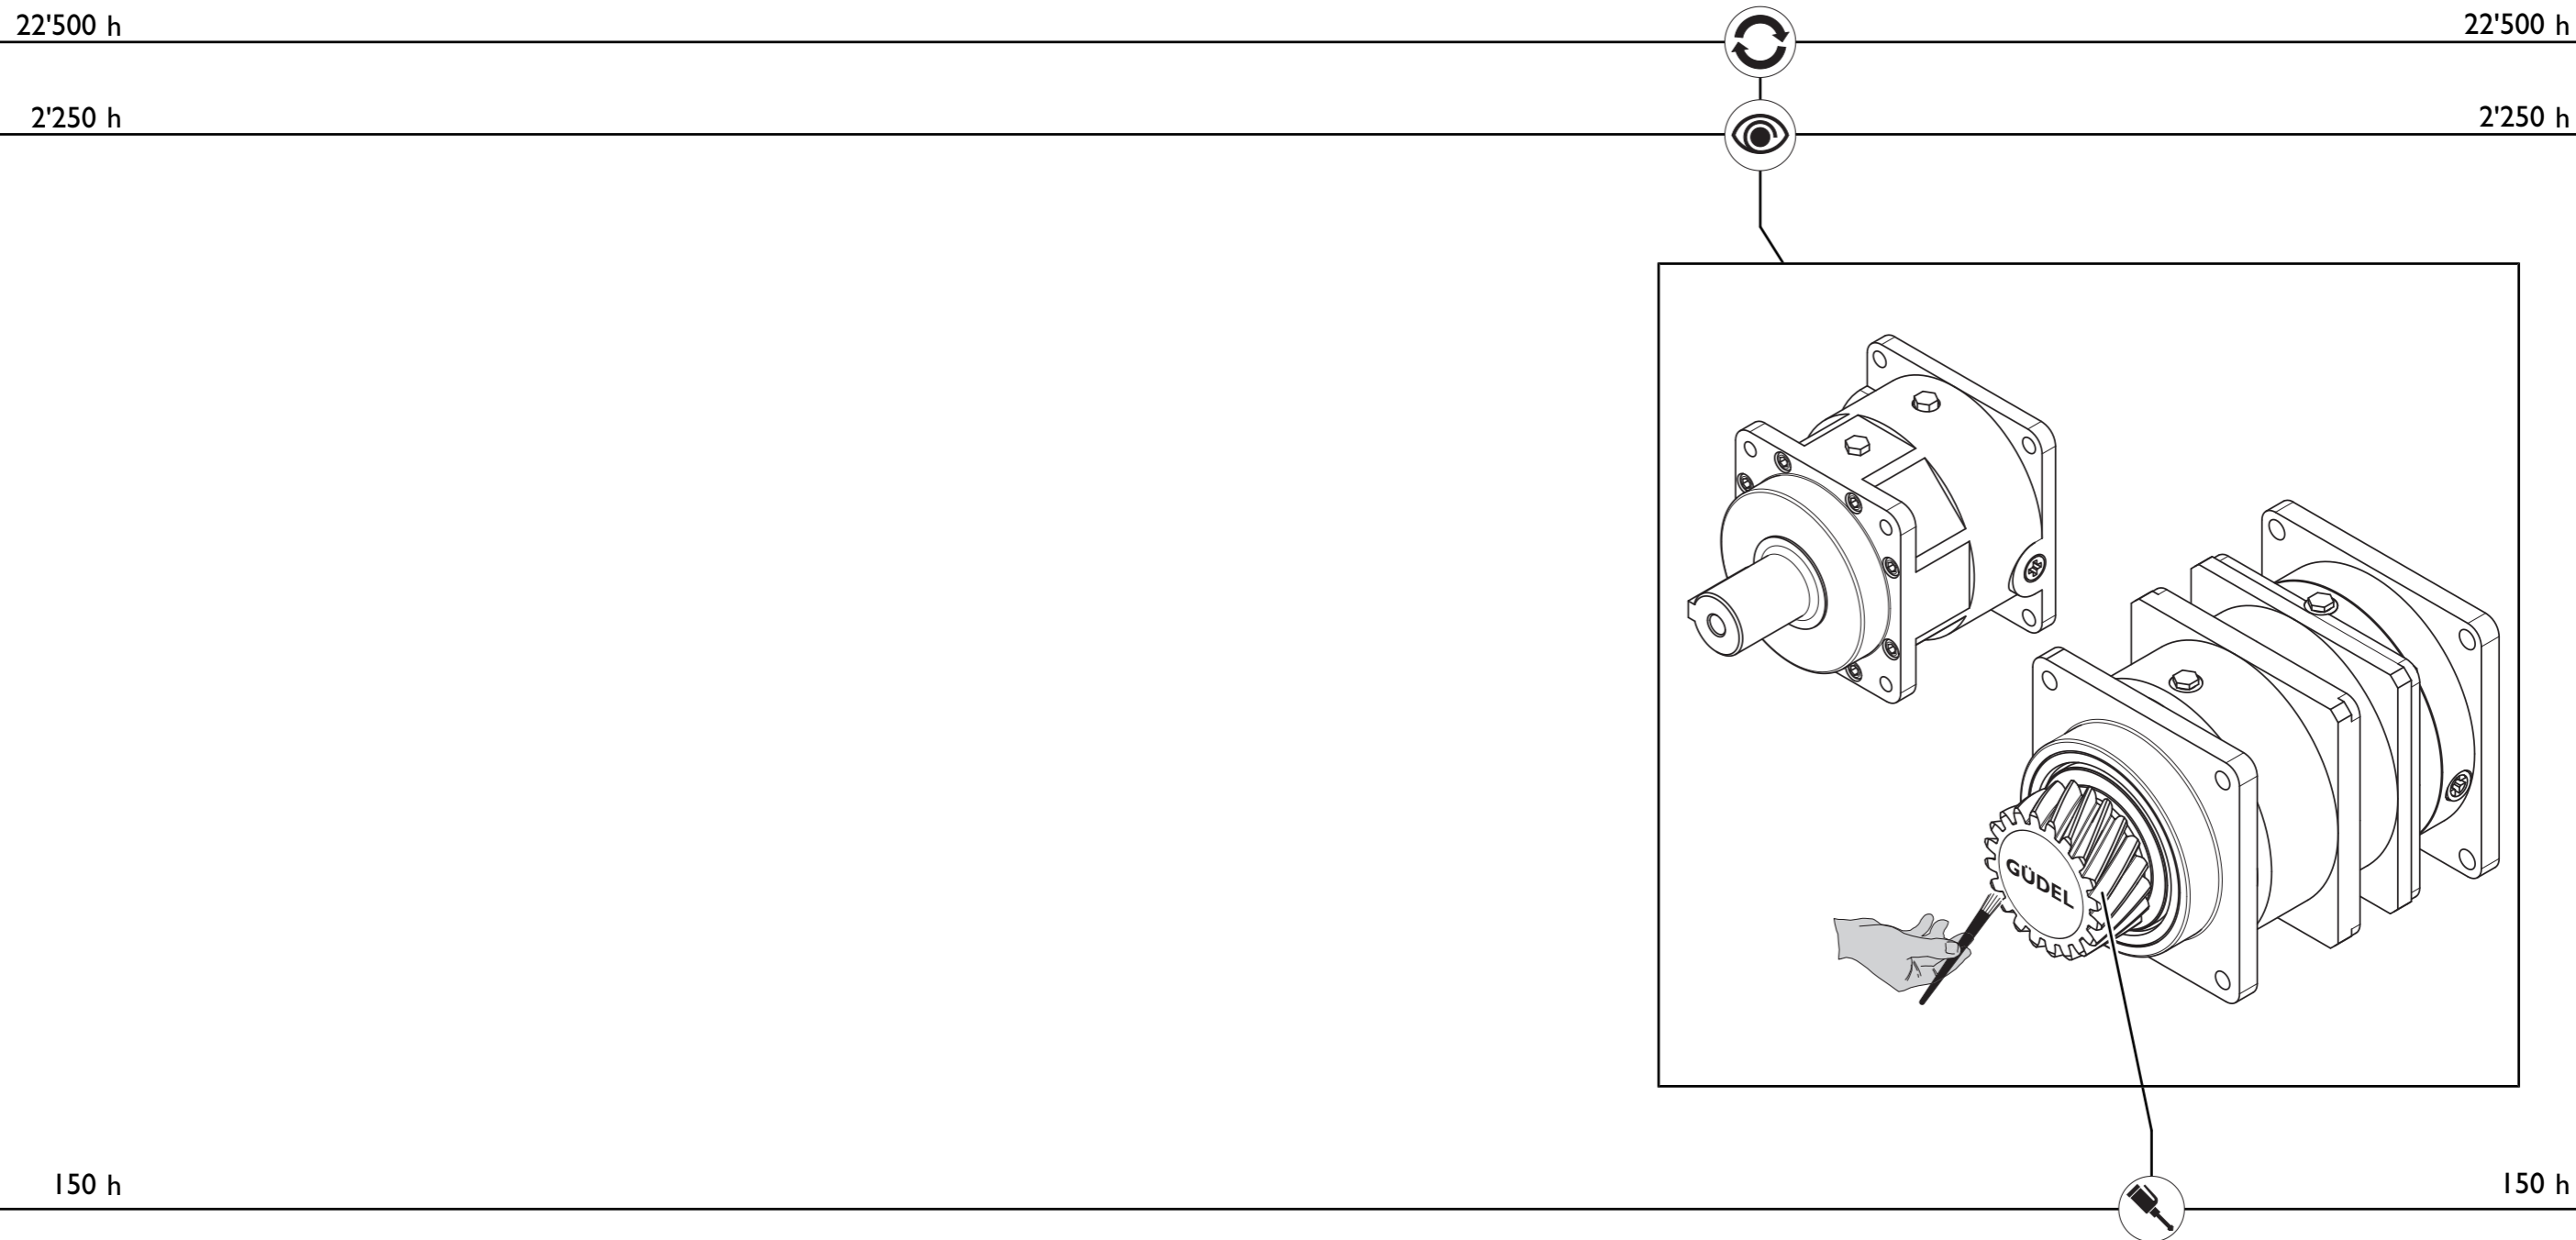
Plan d'entretien : Engrenage planétaire NR, SR, PR
